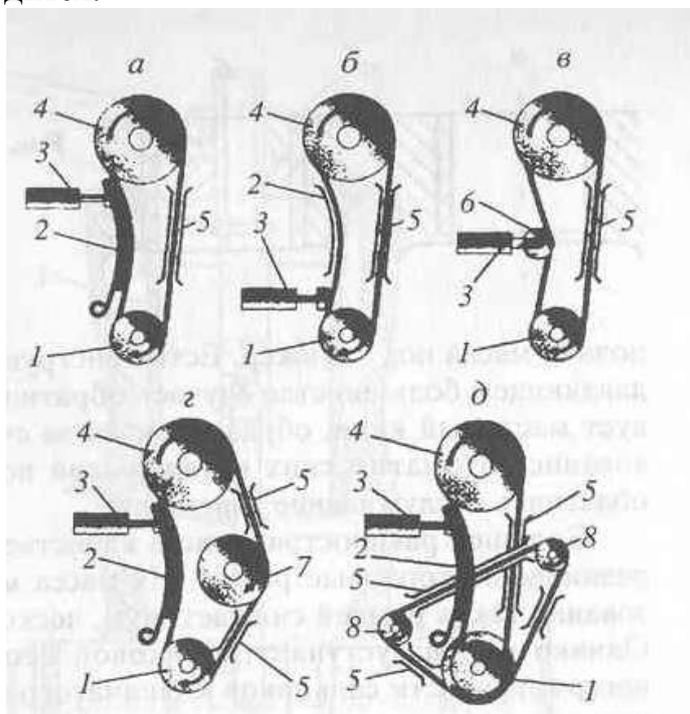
Схема привода распределительного вала роликковой цепью.
